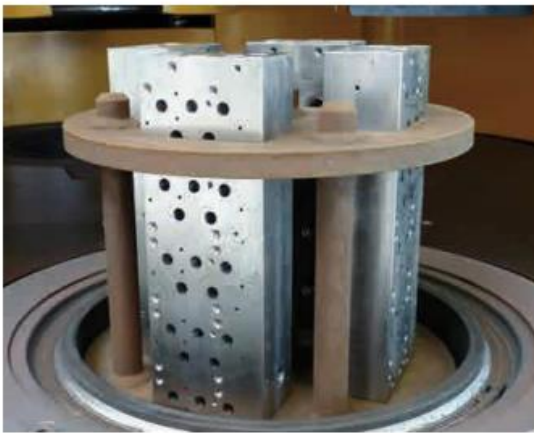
Приклади розміщення деталей у робочій камері під час термоенергетичної обробки
